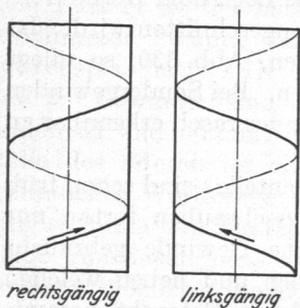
Rechts- und linksgängige Schraubenlinien.
